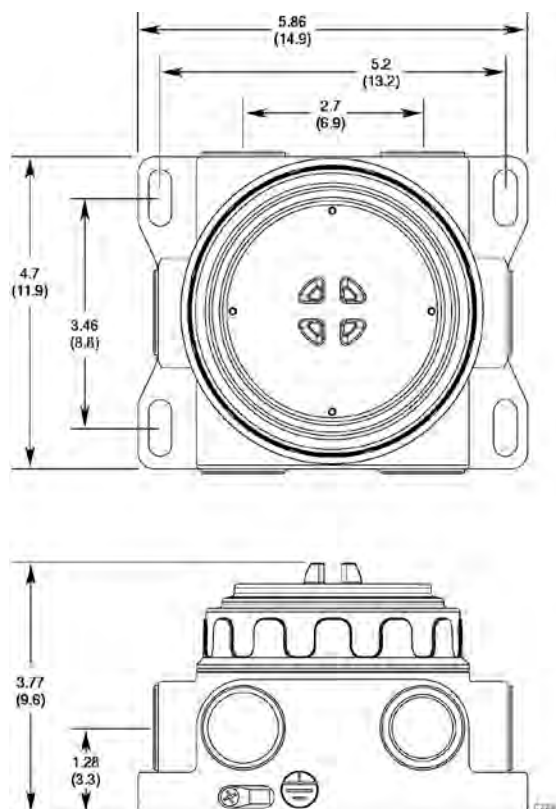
Габаритные и установочные размеры соединительной коробки STB в дюймах (сантиметрах).
